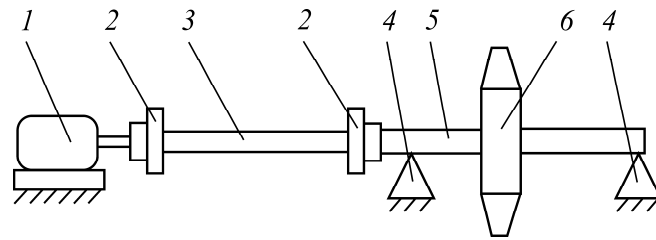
Одноступенчатый осевой вентилятор главного проветривания: 1 — двигатель; 2 — муфта; 3 — трансмиссионный вал; 4 — опоры вала рабочего колеса; 5 — вал рабочего колеса; 6 — рабочее колесо
